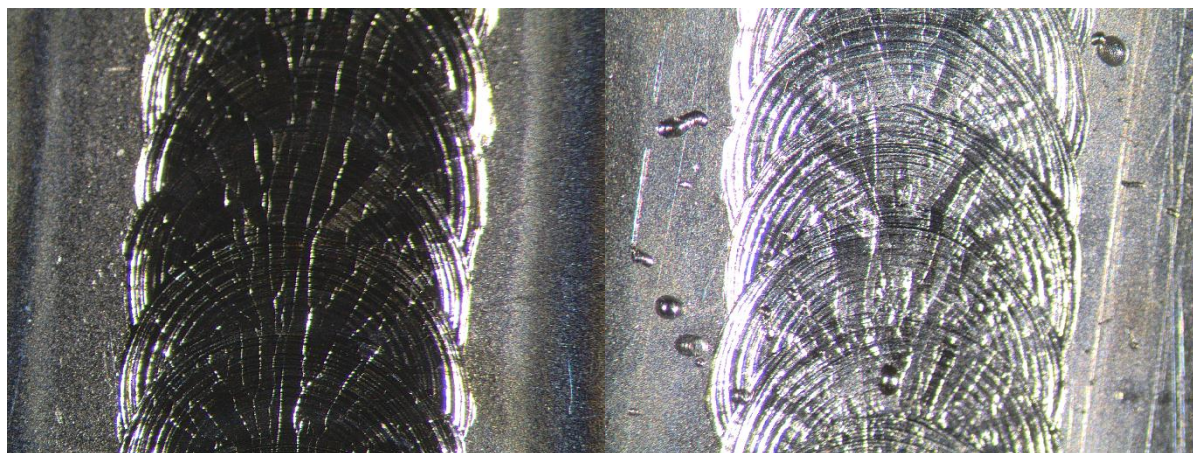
Дефекты при сварке на токе I = 110 А
